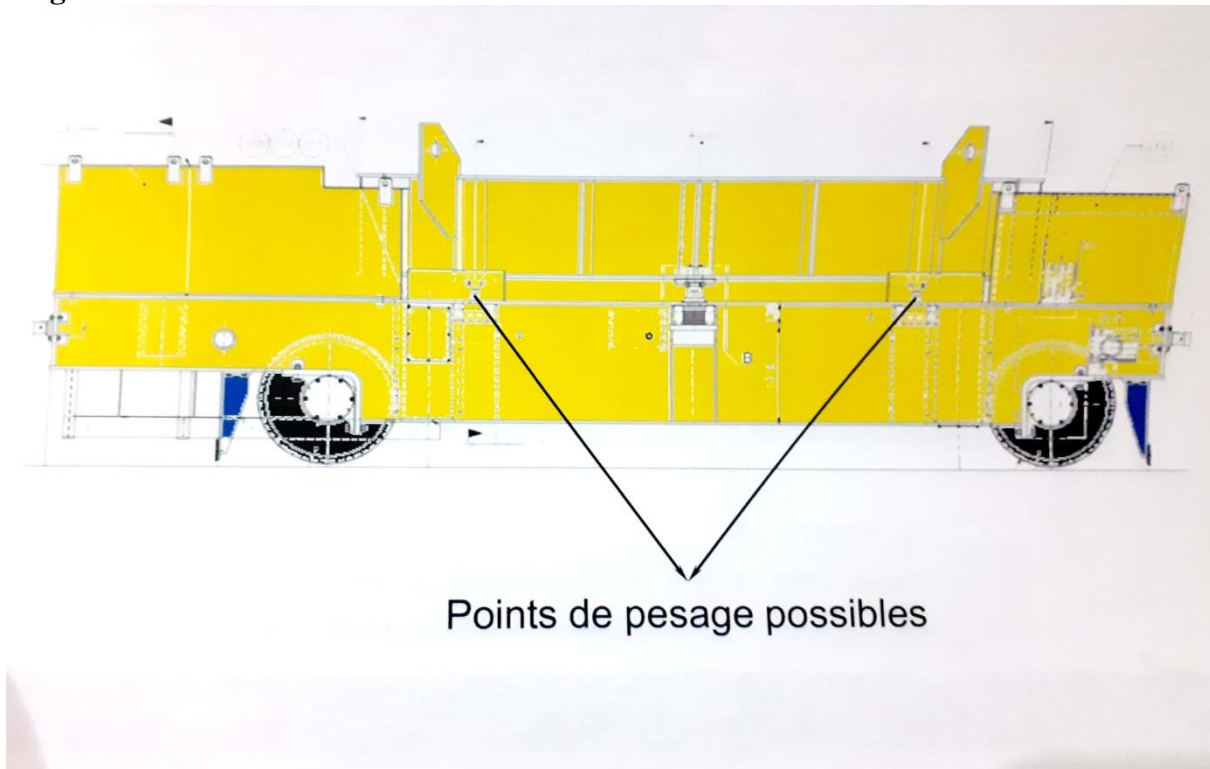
Schéma représentatif du Wagon à ferrailles. [19]
